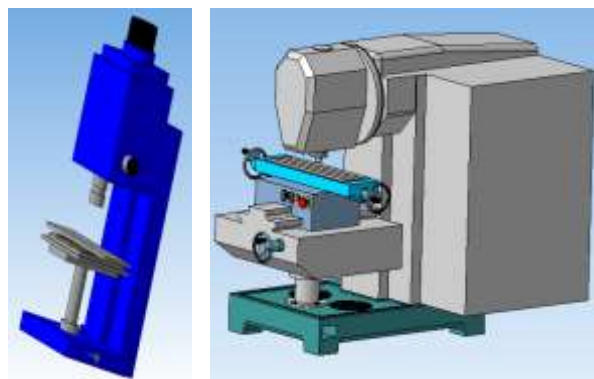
Примеры трехмерных моделей сверлильного и фрезерного станков
